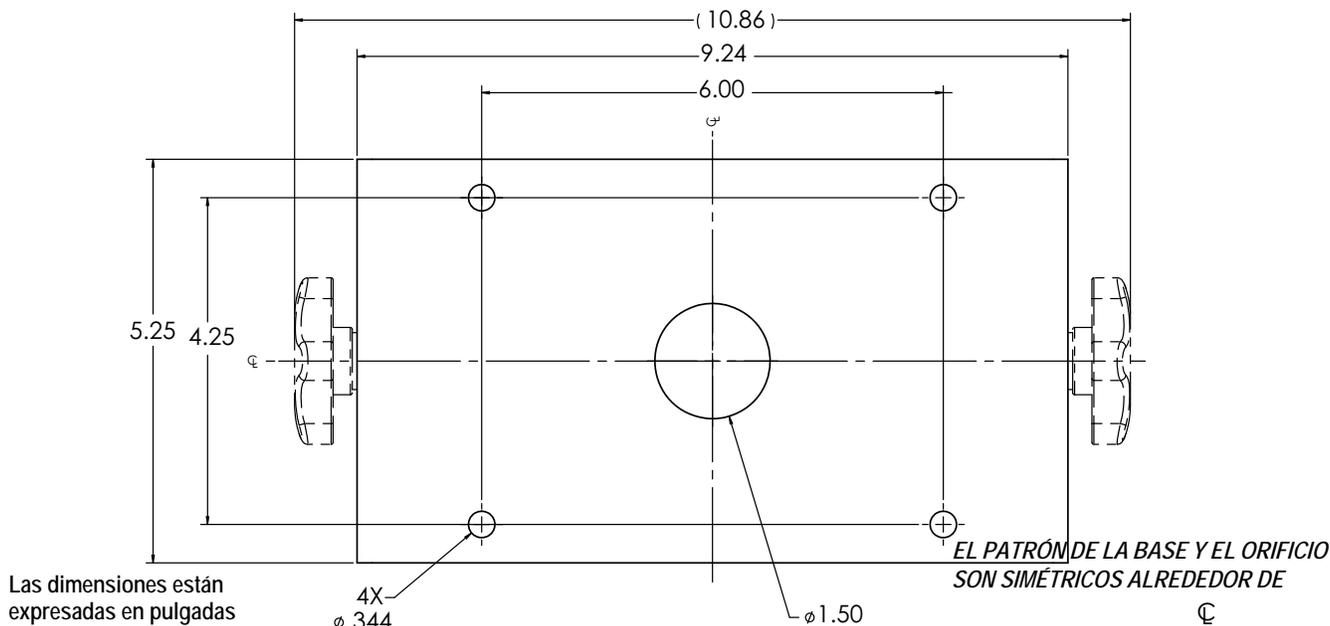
Dimensiones del soporte de montaje en superficie universal
